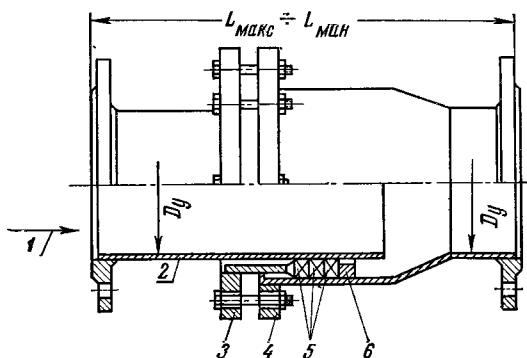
Компенсатор сварной сальникового типа, который используется и как монтажная вставка:
